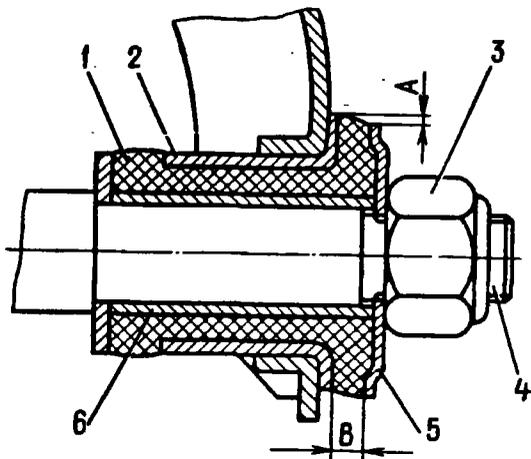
Проверка состояния резинометаллического шарнира рычага передней подвески: 1 - резиновая втулка шарнира; 2 - наружная втулка шарнира; 3 - гайка крепления оси рычага подвески; 4 - ось рычага подвески; 5 - упорная шайба шарнира; 6 - внутренняя втулка шарнира
